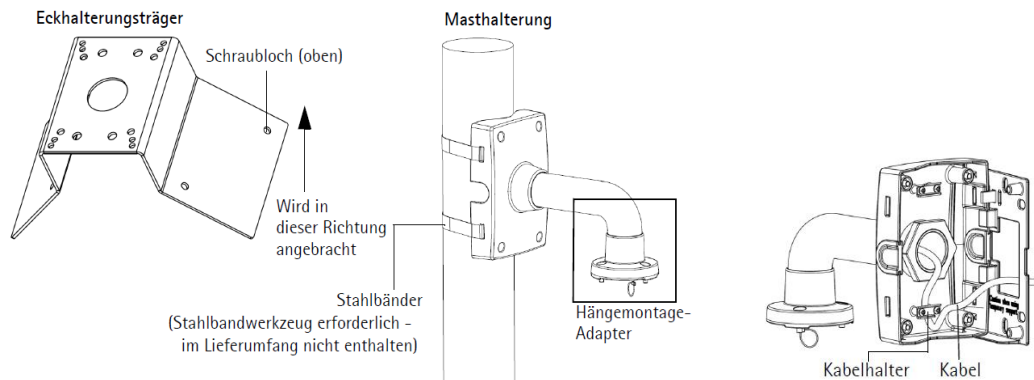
Montageelemente AXIS T91A, Eckbefestigung, Masthalter, Montagearm für AXIS Q60 Serie
